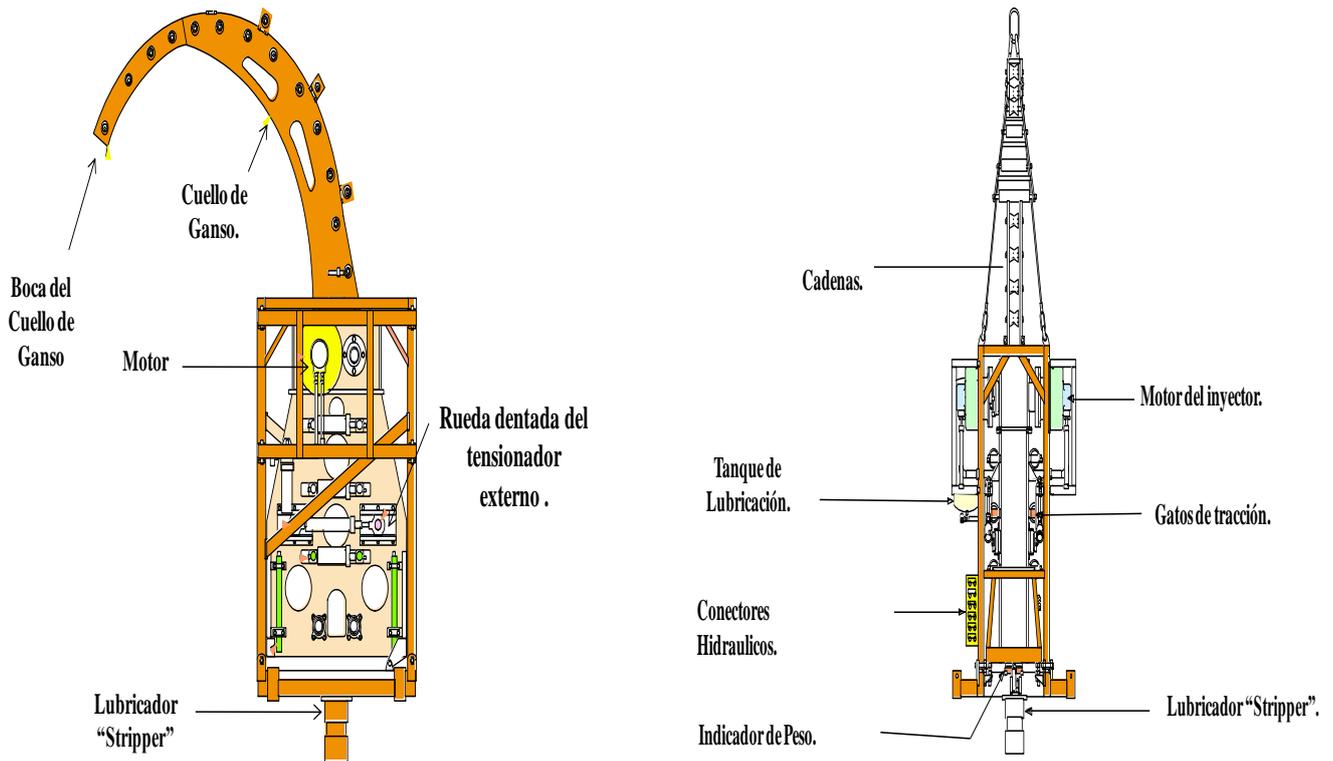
Cabeza inyectora, muestra cada una de las partes que la componen.
